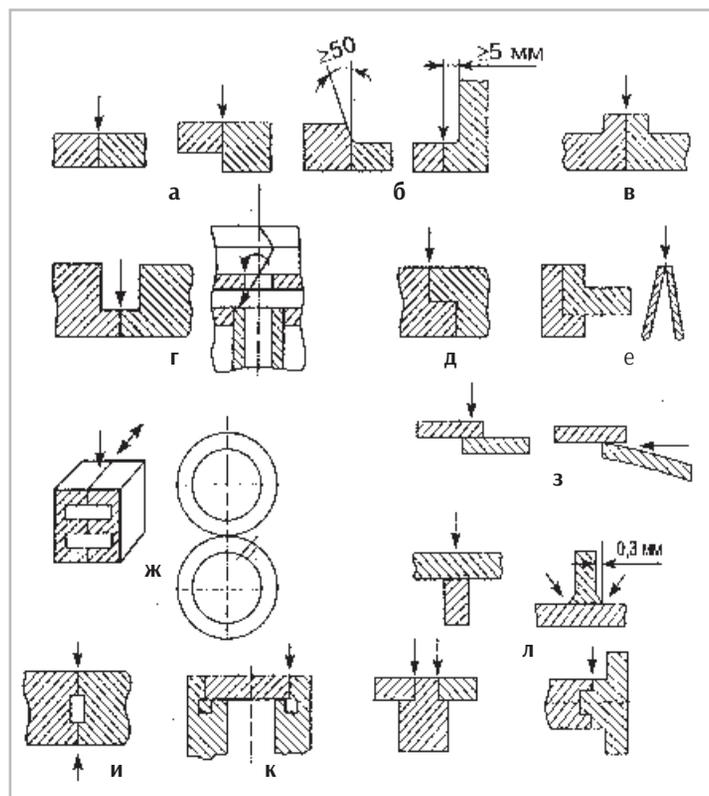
Типы соединений при ЭЛС: а — равнотолщинный стык; б — разнотолщинные стыки; в — стык с отбортовкой кромок; г — стыки в углублениях; д — замковый стык; е — стыковое соединение тонкостенных деталей; ж — «многоэтажные» стыки; з — нахлесточные соединения; и — стык под двухстороннюю сварку; к — стыковое соединение под сварку заглушек; л — тавровое соединение
